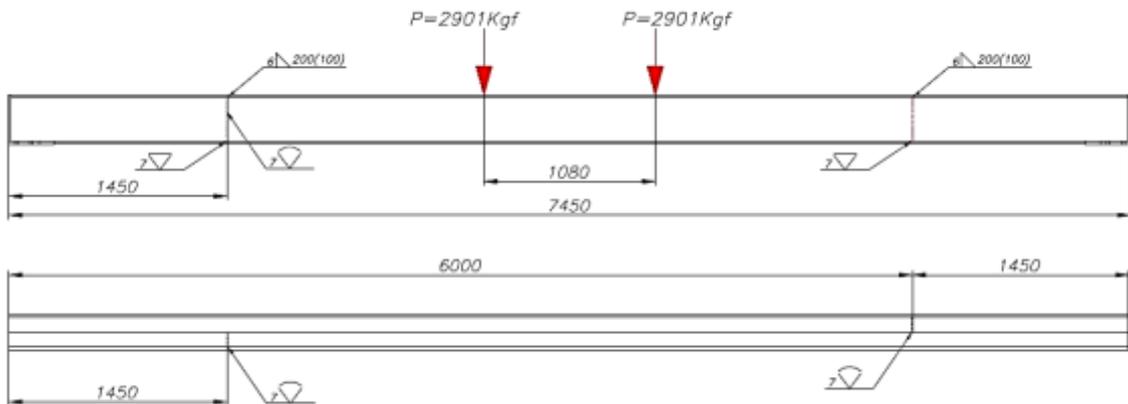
Soldadura en viga puente. Fuente: (Autor)
